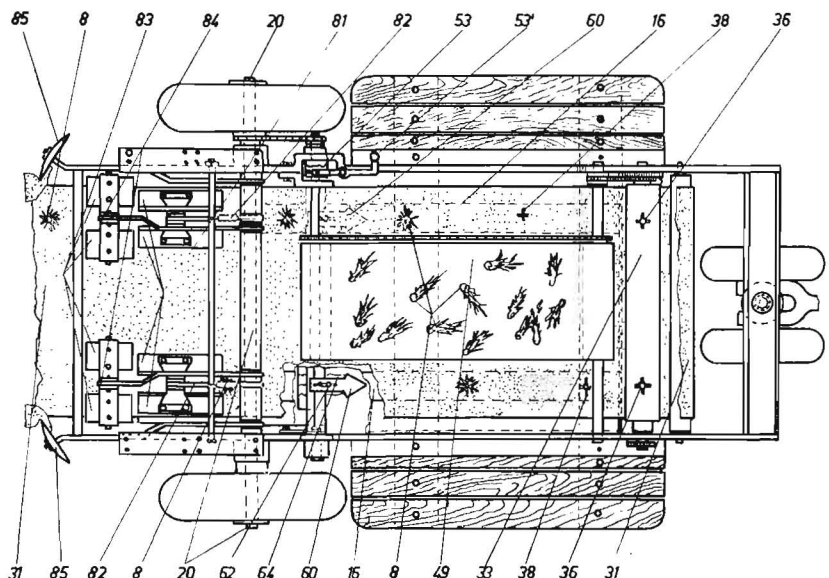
Eine Draufsicht auf die Maschine nach Bild 7
